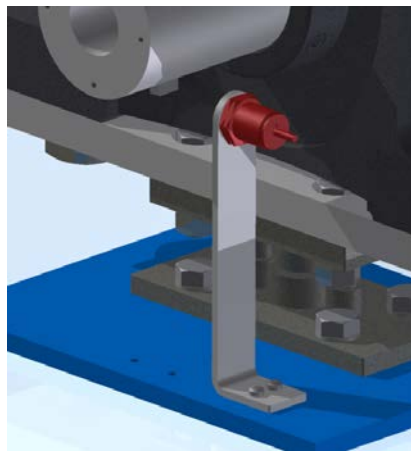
En vermell, sensor de posicionament, en gris, el suport i la pestanya de posició soldada a l'eix.
